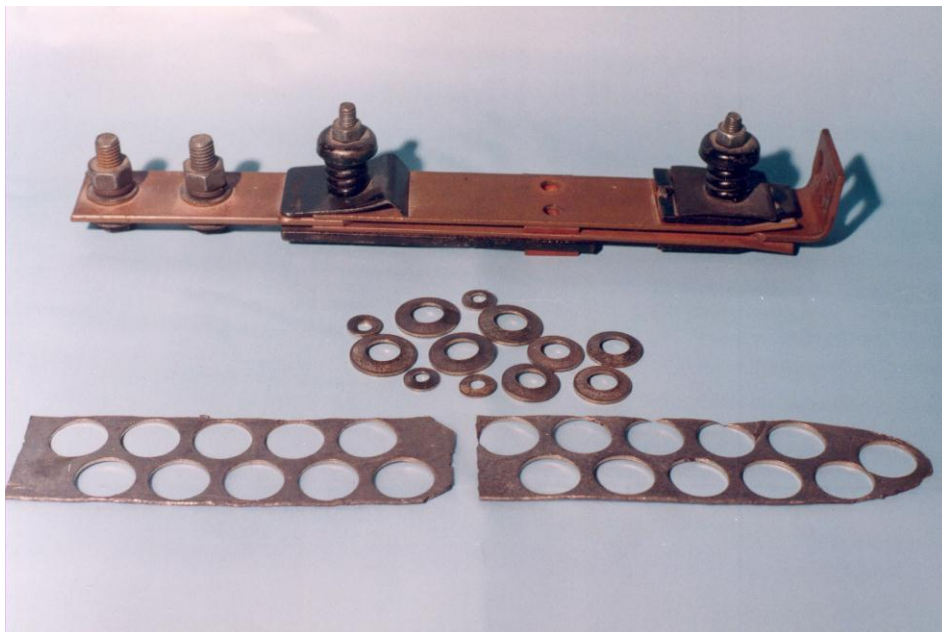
Загальний вигляд конічних шайб, смуги після штампування та контактного з'єднання роз'єднувача з вмонтованими шайбами із сплаву з ЕПФ
